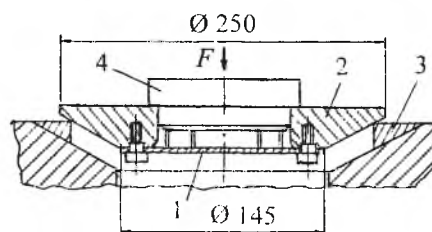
Схема испытаний дисковидного образца: 1 – дисковидный образец; 2 – сектор захвата; 3 – опорный элемент; 4 – пуансон.
